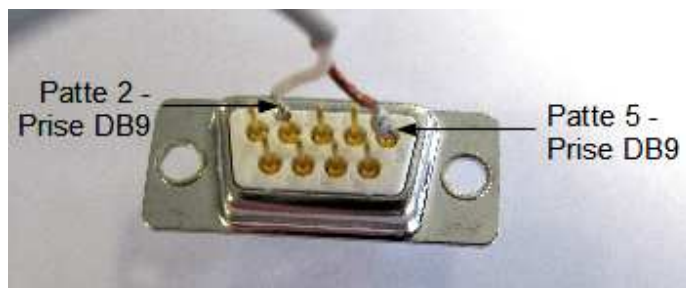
Connexion entre la sortie du PIC et la prise DB9
